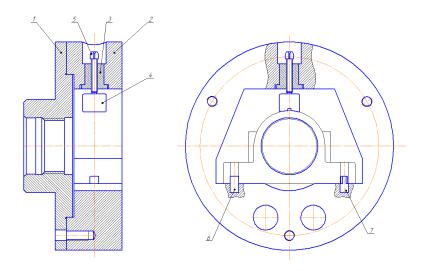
Приспособление для обработки корпуса на токарном станке
